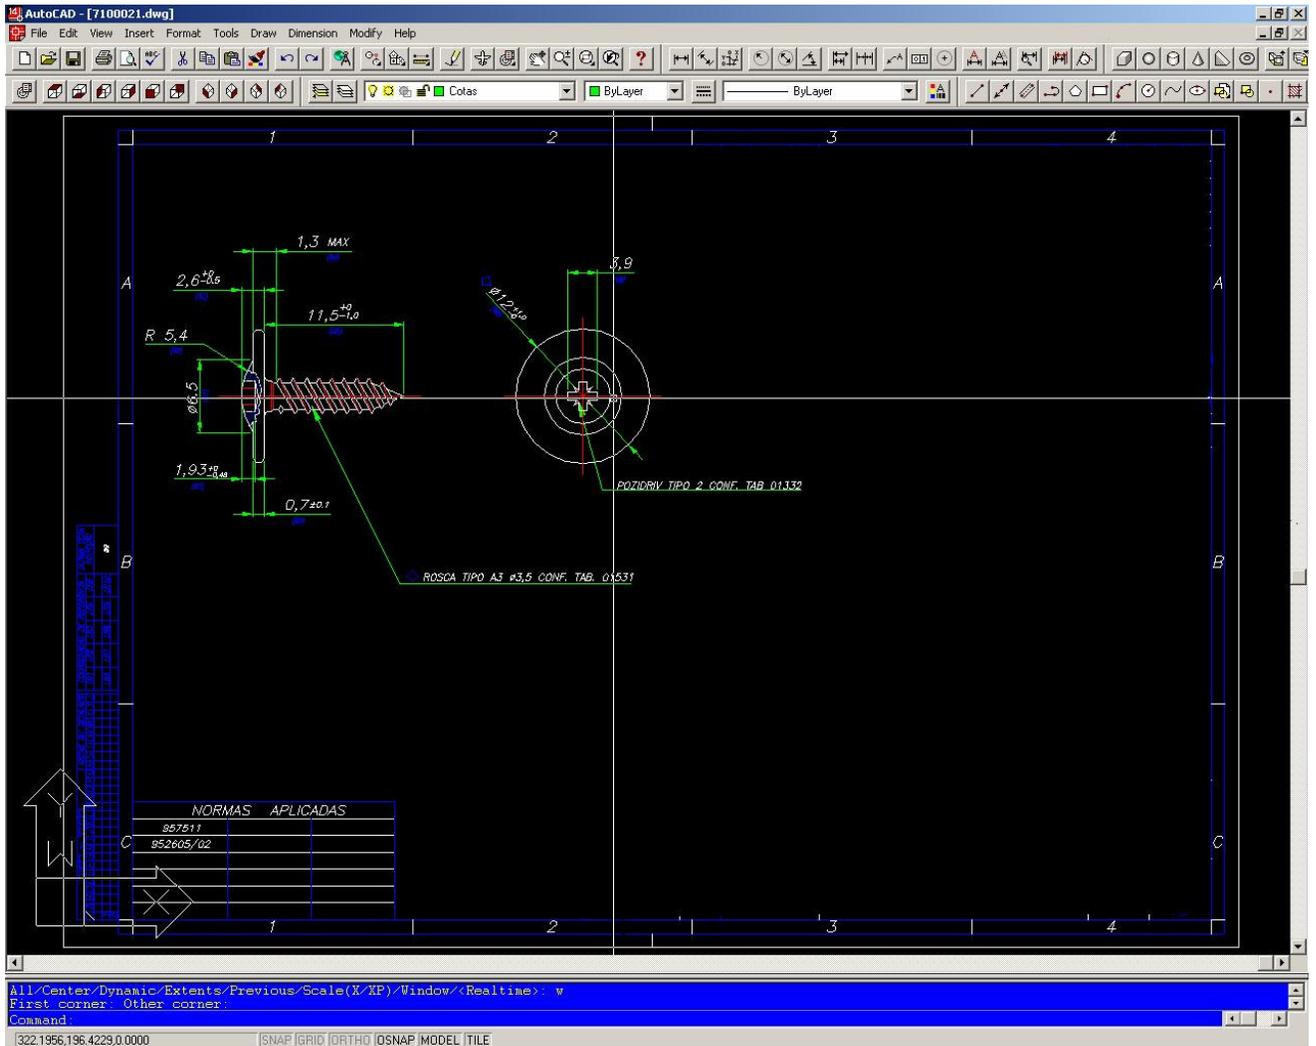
Exemplo de Desenho no Sistema CAD AUTO CAD
